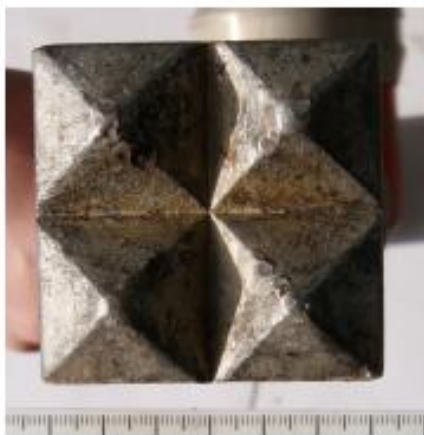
Рельеф торцевой поверхности упора штока гидроцилиндра двухстороннего действия ЦГ-1/80
